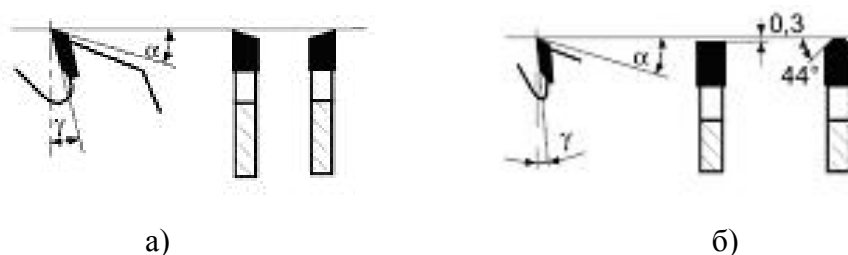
Профили зубьев дисковых пил с пластинами твердого сплава для распиловки ламинированных ДСтП: а – попеременно косой; б – плоско-трапециевидный
